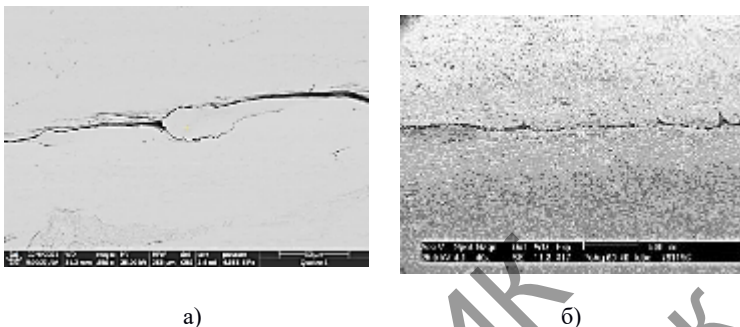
Дефекты в районе сварного шва в виде трещины на внутренней поверхности трубки (а) из сплава ПдСр60-40 и складки на наружной поверхности (б)
